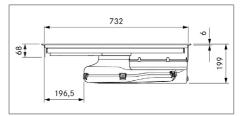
PURU dimensioni apparecchio vista frontale
